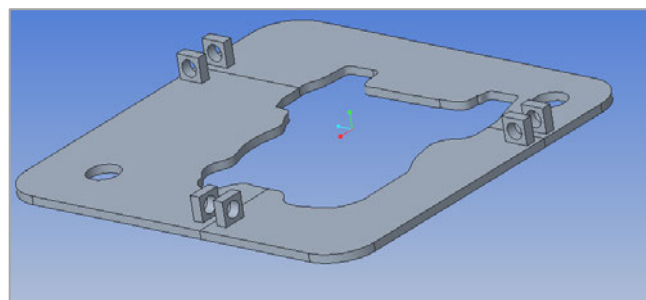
obere Platte mit Bohrungen für das Kühlsystem
